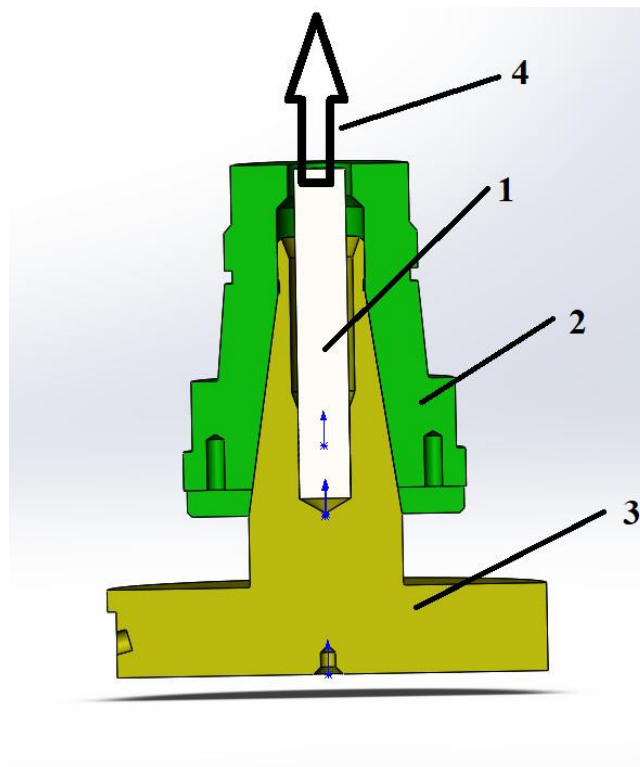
Конічне з'єднання фрези та шпинделя верстата, де 1 – шомпол; 2 – частина шпинделя верстата; 3 – фреза; 4 – напрямок дії зусилля від затягування (закручування різі) шомпола.
